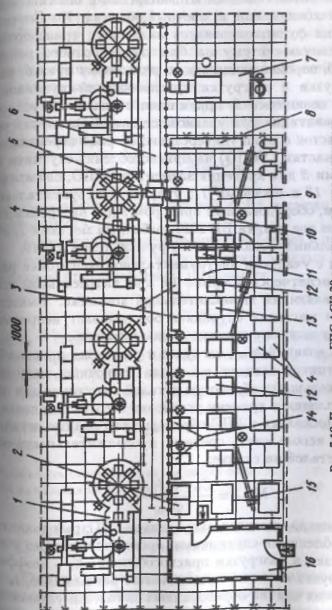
Планировка ГПС АСК-20 для изготовления корпусных деталей в условиях мелкосерийного производства
